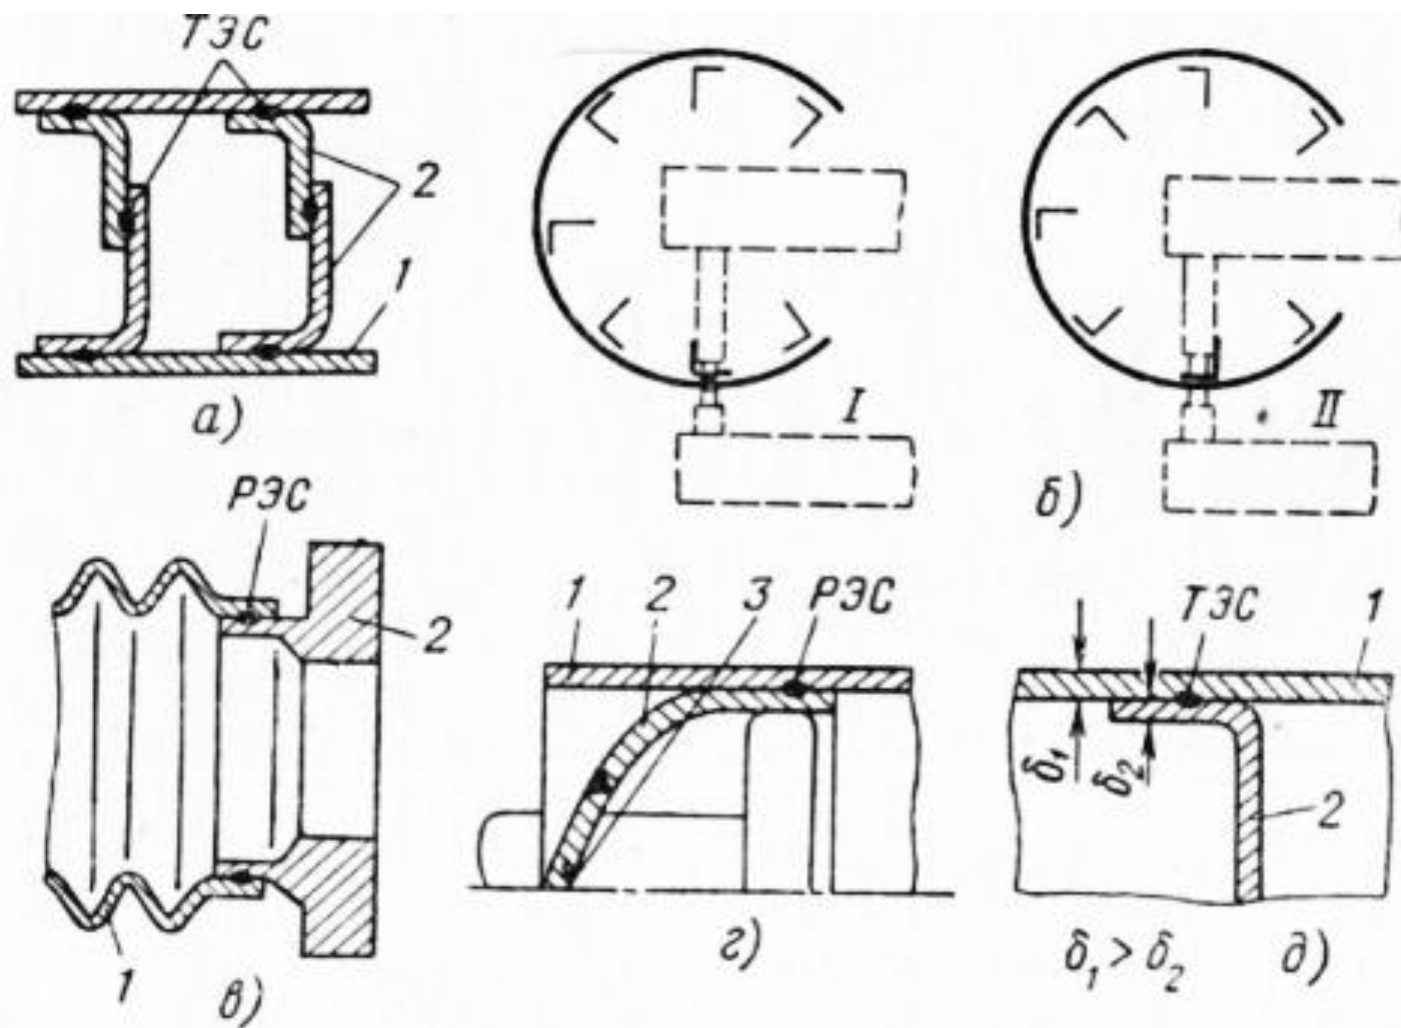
Примеры технологичных конструкций сварных узлов, выполняемых контактной сваркой, ТЭС и PЭС
